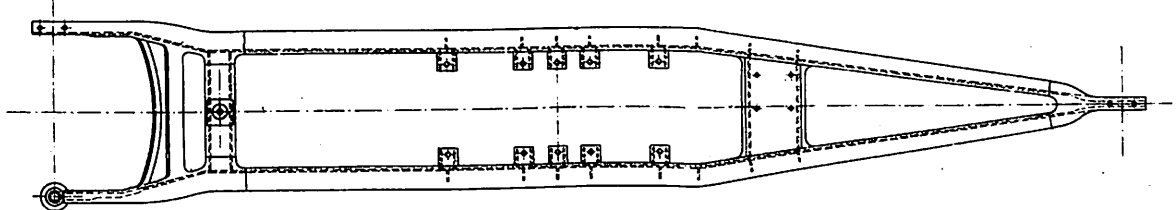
Tragrahmen für eine dieselhydraulische Maschinenanlage mit einem Dr...
